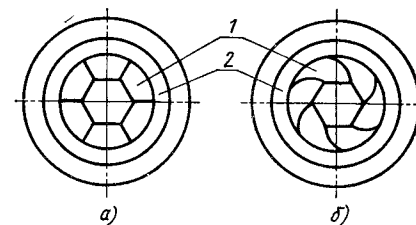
Схемы сборных матриц для штамповки многогранных деталей: а — с плоским радиальным разрезом; б — с криволинейной поверхностью разреза
